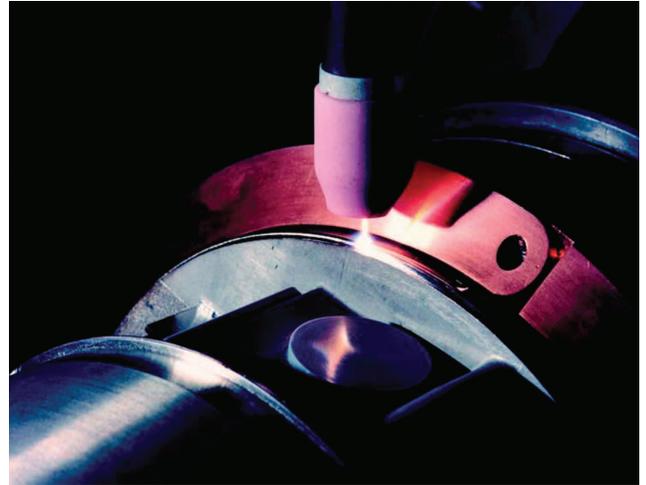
soldadura GTA autógena en dos piezas fundidas mecanizadas de acero inoxidable 17-4PH para la industria aeroespacial.
